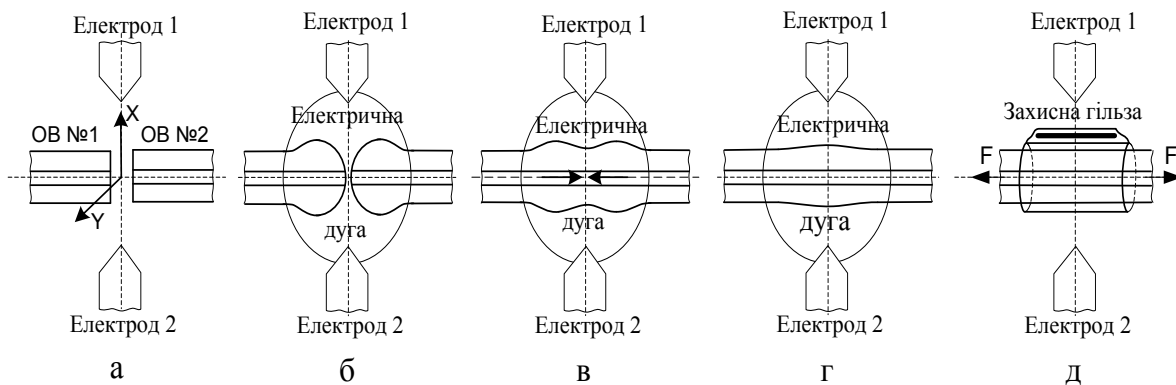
Етапи зварювання ОВ: а – юстування ОВ;
